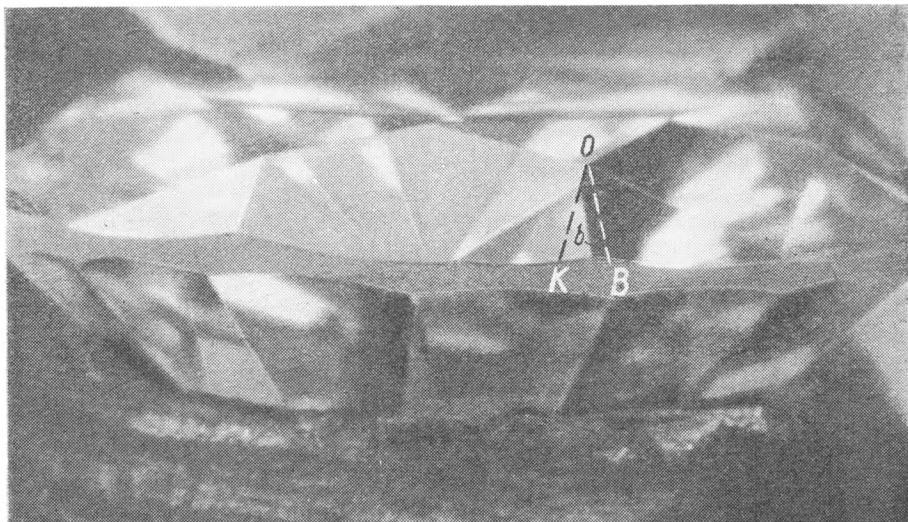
Шлифовка правого парного клина верха на угловой грани верха.
